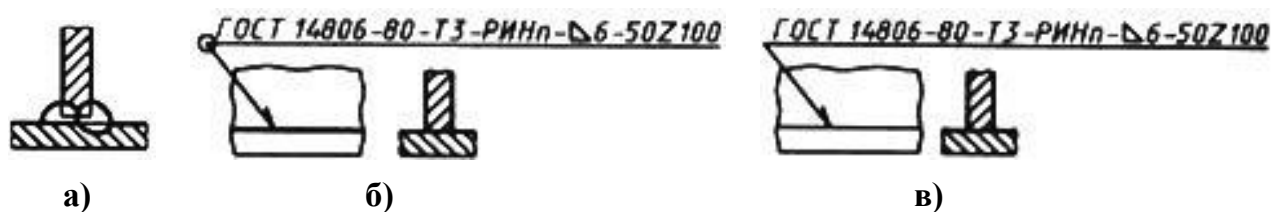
Пример обозначения сварного шва [5]: а – форма поперечного сечения шва; б – обозначение с лицевой стороны; в – обозначение с оборотной стороны
